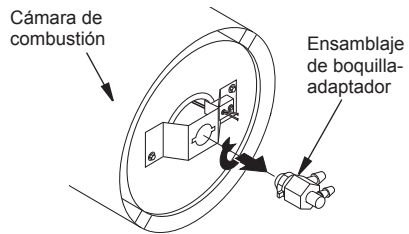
Desmontaje del ensamblaje de boquilla-adaptador
